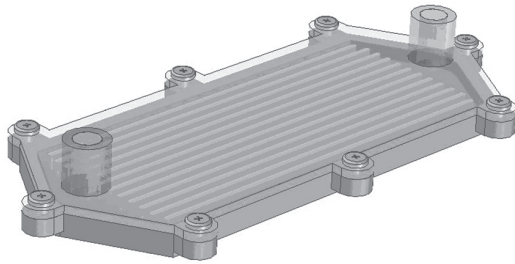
DISIPADOR LADO CALIENTE DISEÑADO
